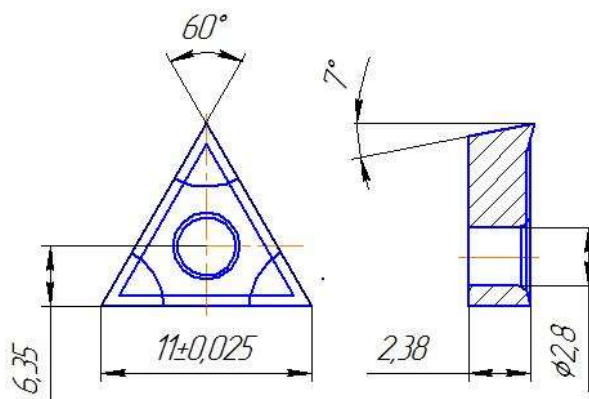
Эскиз твердосплавной пластины
